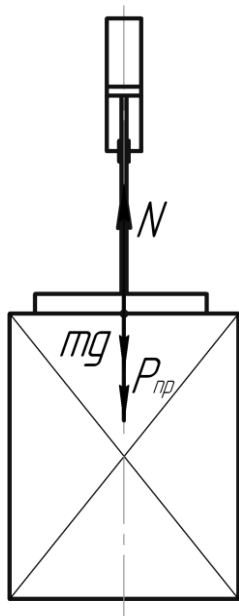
Розрахункова схема для підбору пневмоциліндра пристрою прижимання пакету
